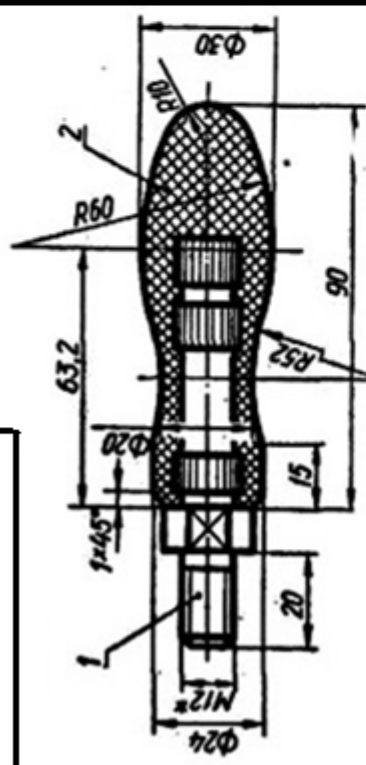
Креслення виробів, виготовлених наплавленням на деталь металу або сплаву
